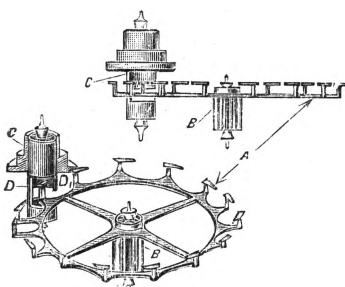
Цилиндрический ход. А—цилиндрическое колесо, В—триб цилиндрич. колеса, С—цилиндр, D—входная губа, D₁—выходная губа.
